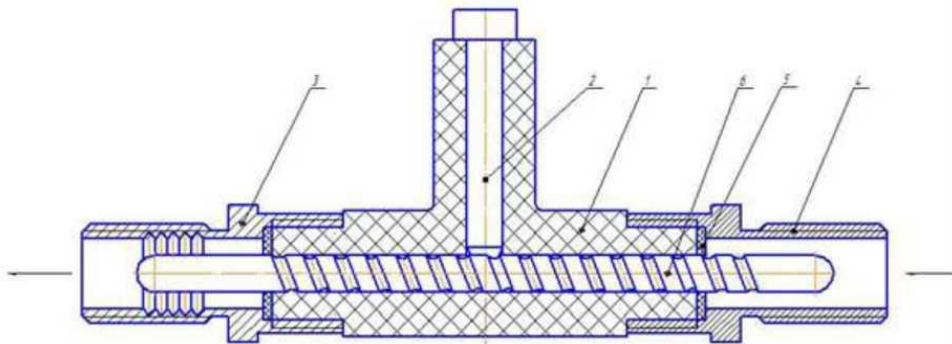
Пристрій для електромагнітної обробки дизельного палива: 1 – корпус; 2 – стержень; 3 – канал випускний; 4 – канал впускний; 5 – прокладення; 6 – електрод позитивний.
